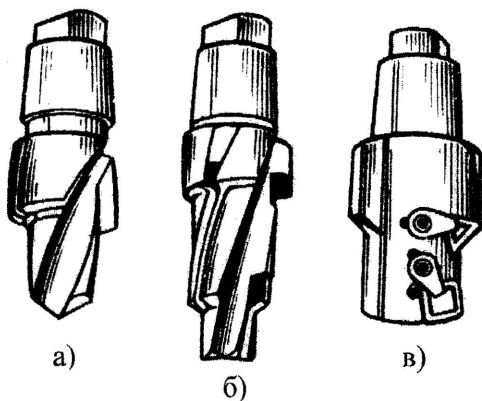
Комбинированные инструменты для обработки отверстий на станках с ЧПУ:
